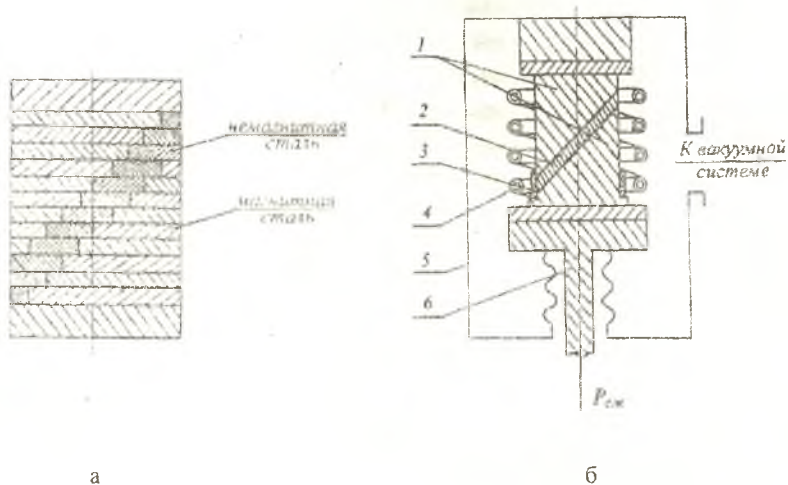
Эскиз биметаллического ротора, изготовленного электронно-лучевой сваркой (а), и схема диффузионной сварки ротора (б): 1 – детали из магнитной стали, 2 – детали из немагнитной стали, 3 – технологическое кольцо, 4 – индуктор, 5 – вакуумная камера, 6 – шток гидроцилиндра
